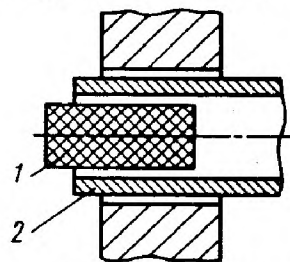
Схема размещения индуктора для крепления труб магнитно-импульсным методом: 1 – специальный индуктор; 2 – закрепляемая труба
